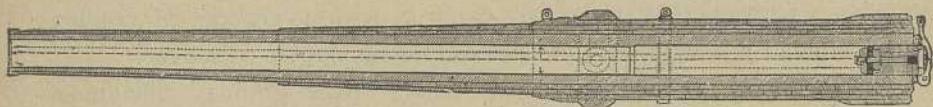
Cañón de De Bange, de 34 centímetros.
